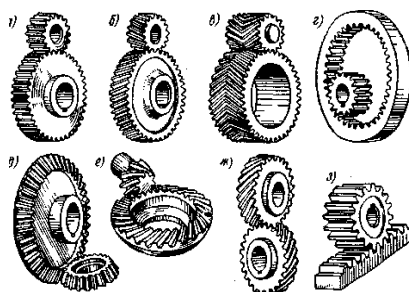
Конструкции цилиндрических зубчатых колес
